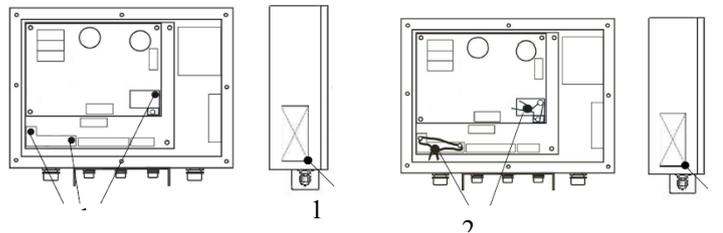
Схема пломбировки корпуса весоизмерительных приборов:
